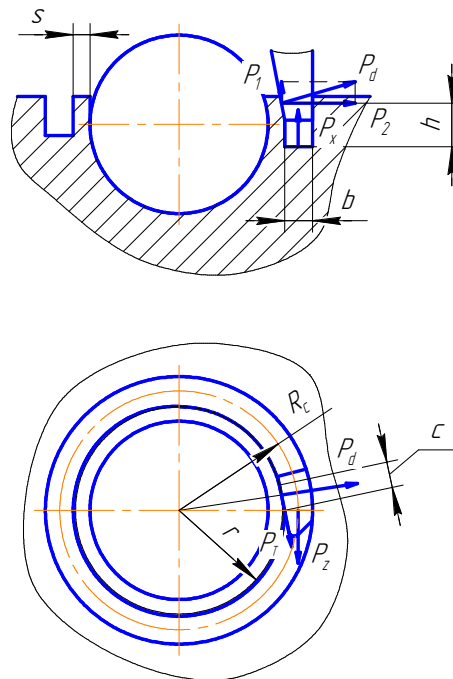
Розрахункова схема для розрахунку інструмента для завальцювання кульки
